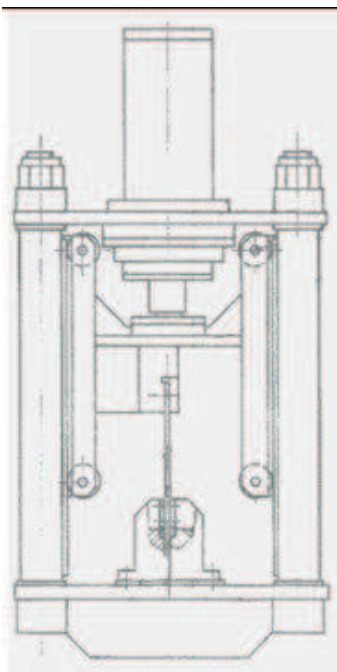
Механизм резания с фигурным ножом и двумя боковыми ножами
